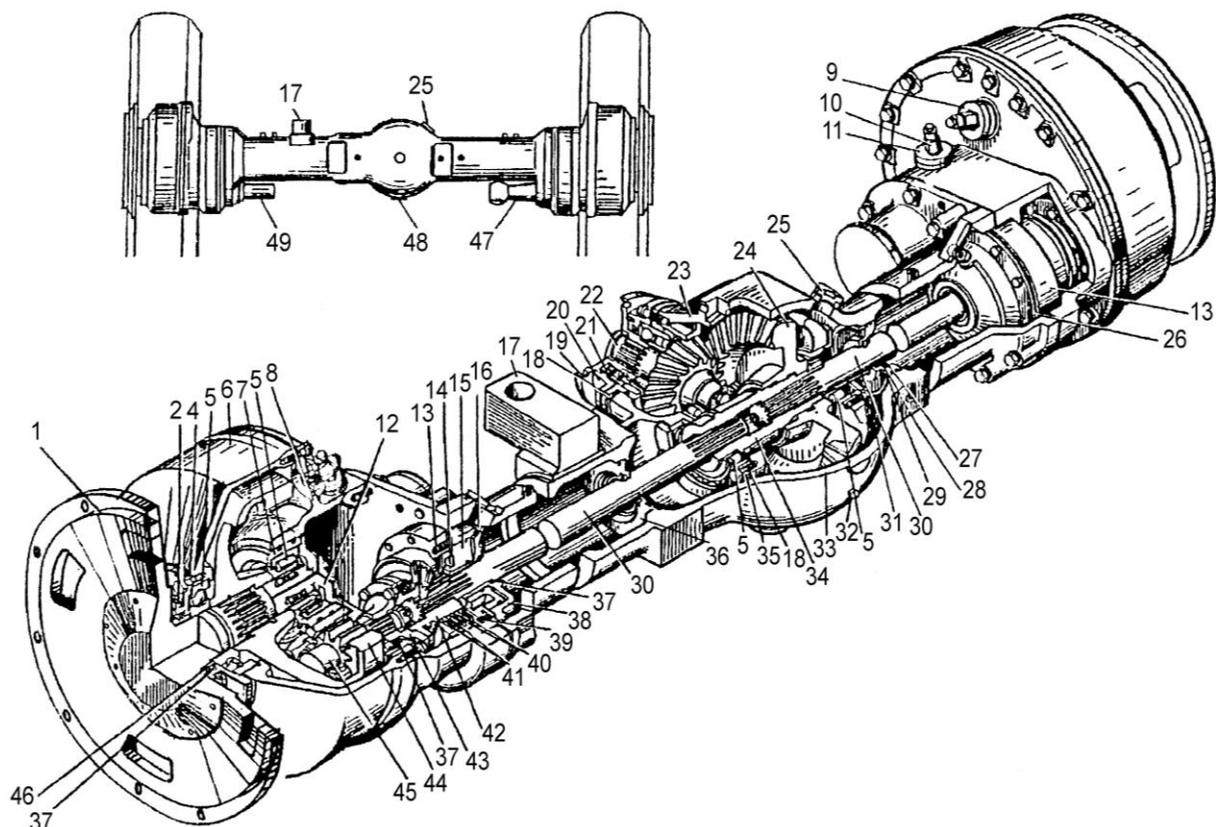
Задний мост: 1 – ступица; 2 – уплотнительное кольцо; 4 – крышка корпуса подшипника; 5 – подшипник; 6 – корпус бортового редуктора; 7 – стакан; 8 – корпус; 9, 11 – пробка заправочного отверстия бортового редуктора, тормоза; 10 – сапун; 12 – крышка подшипника ступицы; 13 – корпус тормоза; 14 – нажимной диск тормоза; 15 – поршень; 16 – штуцер; 17 – кронштейн крепления реактивной штанги; 18 – регулировочные прокладки; 19 – фланец главной передачи; 20, 31, 35 – крышки подшипников; 21 – маслоотражательная шайба; 22 – вал-шестерня главной передачи; 23 – кронштейн; 24 – шестерня; 25 – пробка заливной горловины главной передачи; 26, 38 – пневмоцилиндр тормоза; 27 – стопорное кольцо; 28 – шайба; 29 – корпус сальника; 30 – полуось; 32 – контрольная пробка; 33 – балка; 34 – шлицевая втулка; 36 – корпус сальника; 37 – манжета; 39 – пружина; 40 – диски с наружным зацеплением; 41 – тормозные диски с внутренним зацеплением; 42 – ведущая втулка; 43 – фланец; 44 – шестерня с внутренним зацеплением; 45 – вал-шестерня; 46 – втулка; 47 – шаровой палец; 48 – сливная пробка; 49 – палец
